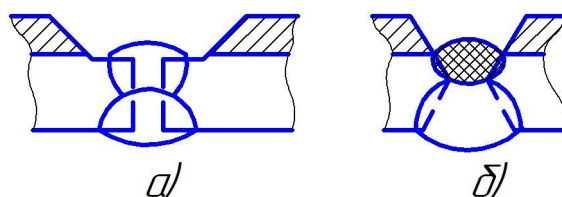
Сварка основного слоя двухслойной стали:
